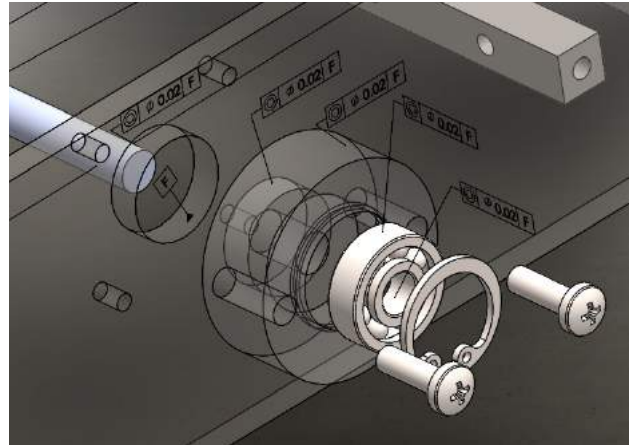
Tolerancia geométrica para alojamiento de rodamiento y rodamiento.
